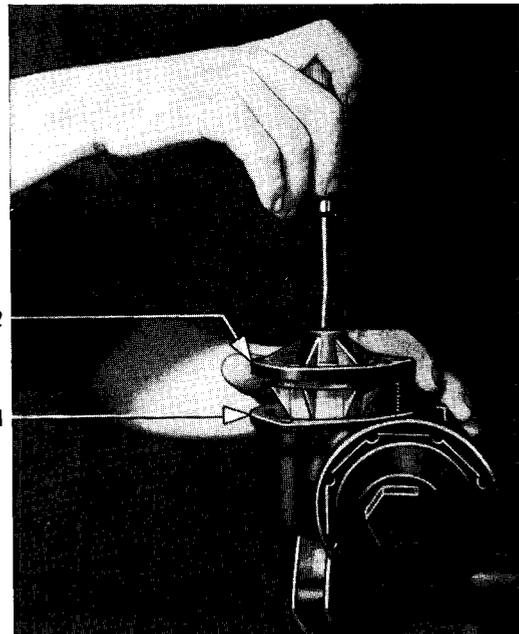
Einstellschraube mit Schraubenzieher in Lenkgehäusedeckel einschrauben (an ausgebauter Lenkung gezeigt)
